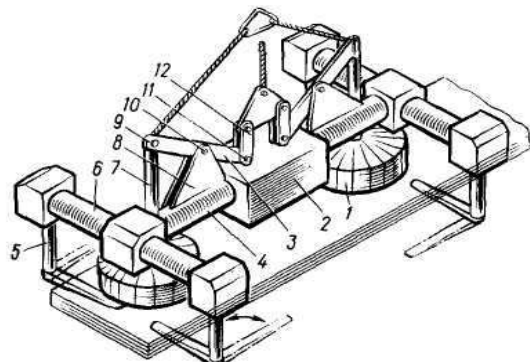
Комбинированный захват для пакетов листовой стали
